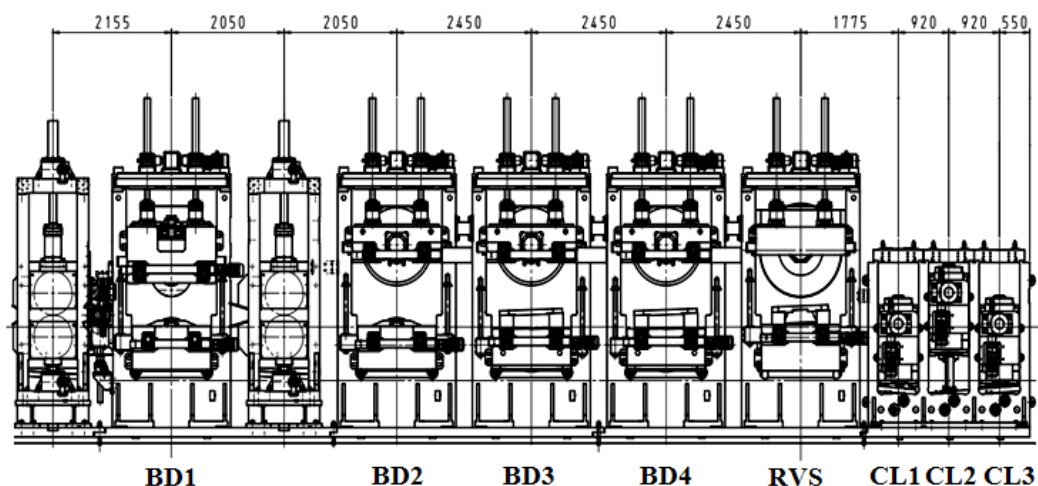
Общий вид формовочного стана знакопеременного изгиба
